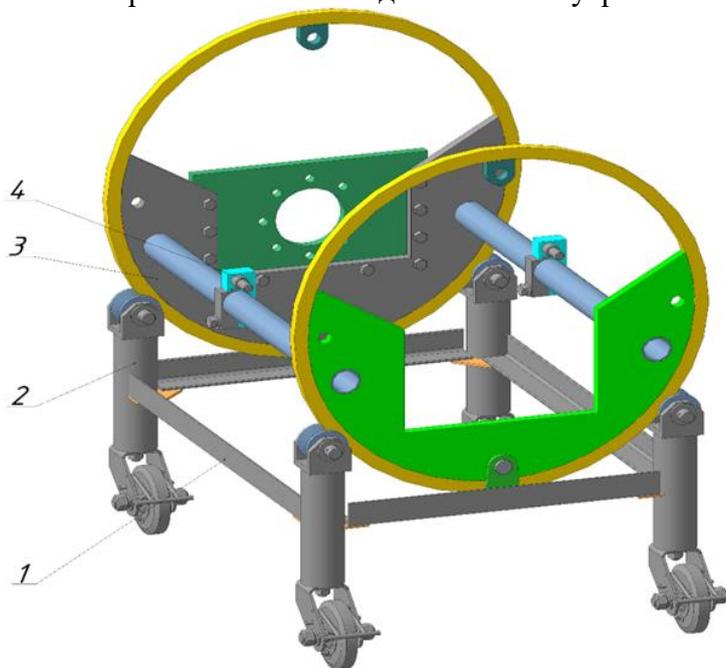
Стенд для ремонта и обкатки ДВС
